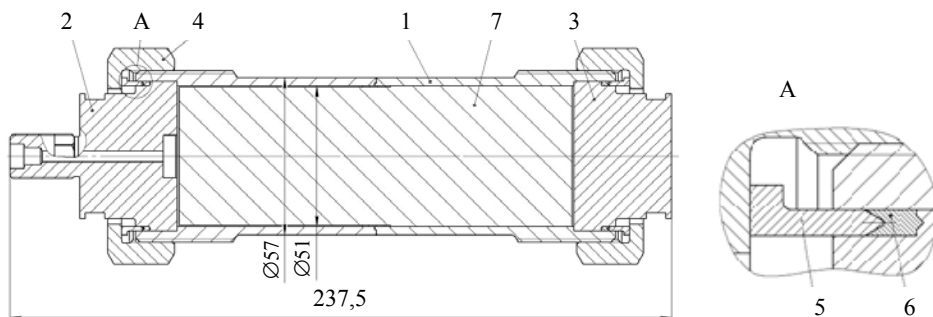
Конструкция прочностного макета из стали 37Г2С: 1 – обечайка; 2, 3 – крышка; 4 – гайка; 5 кольцо; 6 – прокладка; 7 – вкладыш
